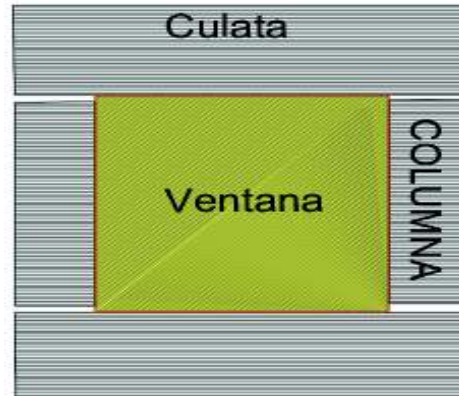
Núcleo, yugo y columnas [autoría propia]
